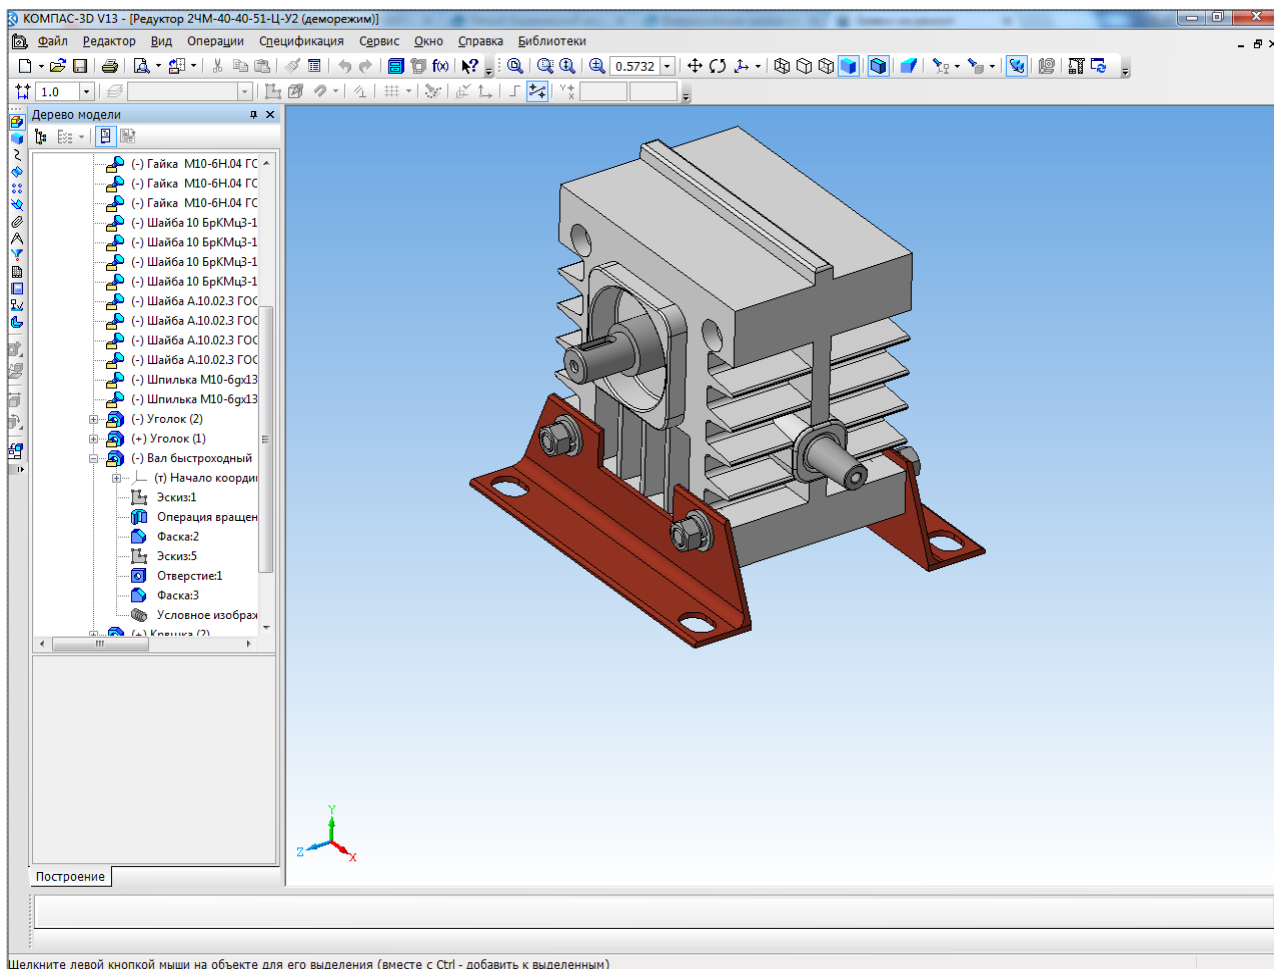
Сборка «Редуктор 2ЧМ-40-40-51-Ц-У2»
